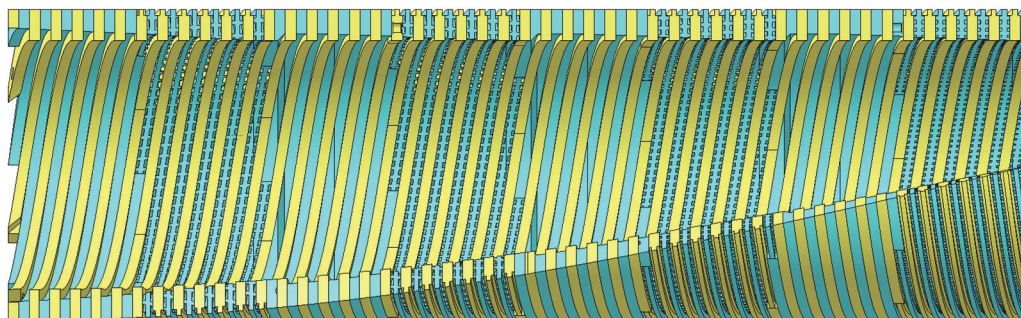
Схема разреза внутреннего устройства перфорированного цилиндра обвального пресса с внутренней поверхностью, образованной канавками на торцевых поверхностях контрвинтовых колец
